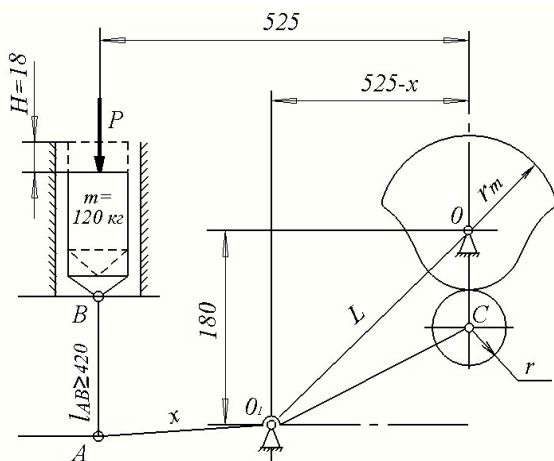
Кинематическая схема механизма подъема корпуса кашировальной колодки блокообработывающего агрегата
